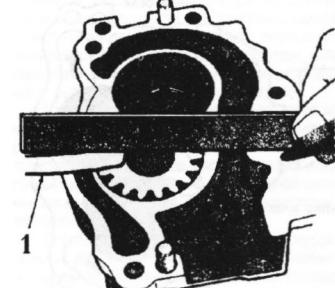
Используйте ровный край и толщиномер для проверки конечного люфта ведомой шестерни
